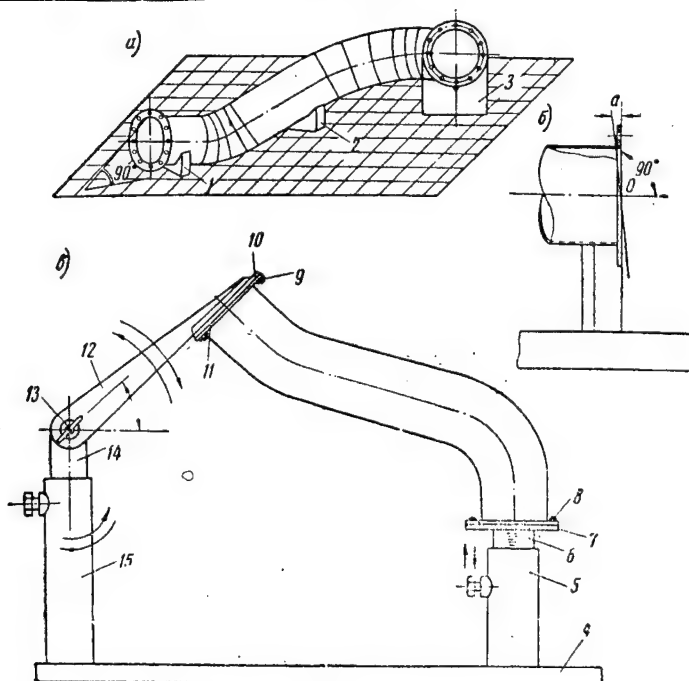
Сборка труб с фланцами: а — разметка установки фланцев на плите; б — установка фланца; в — позиционер.
